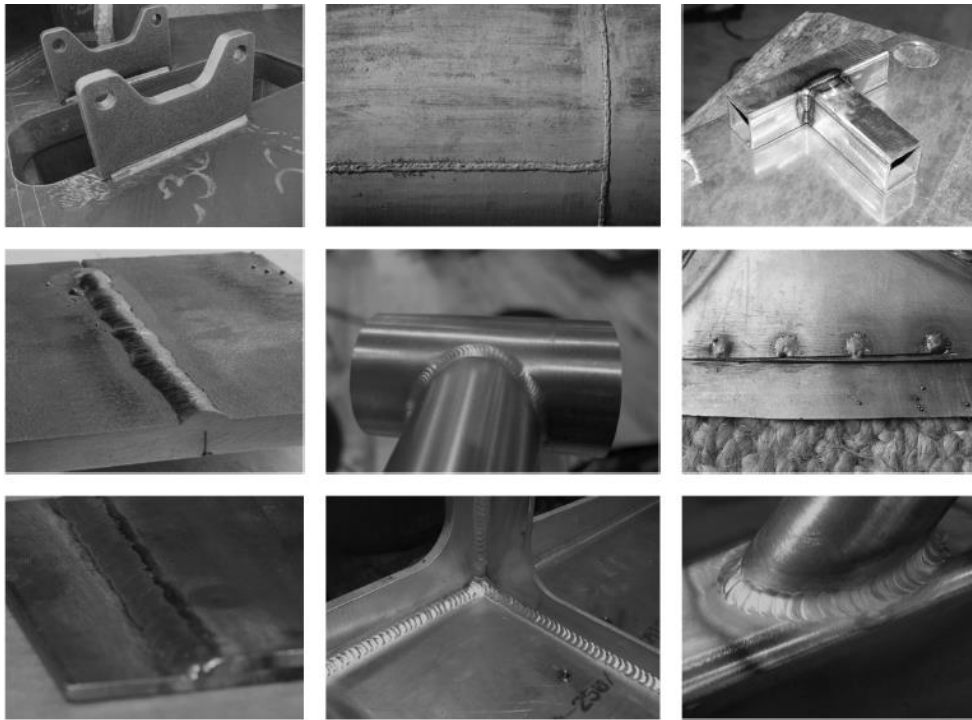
Exemplos reais de vários tipos de soldadura [16]
